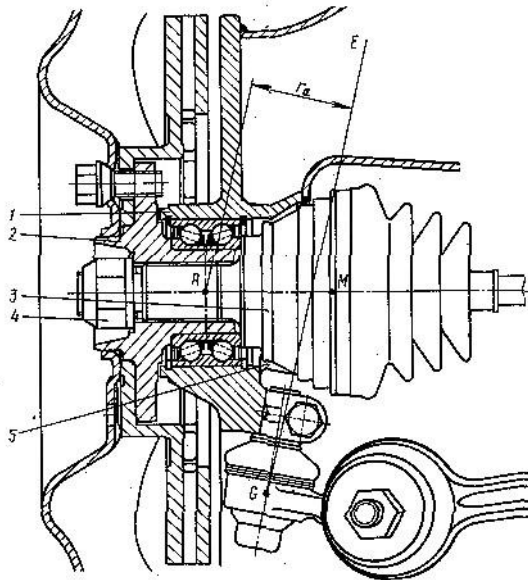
Опора переднего колеса автомобиля «Форд-Фиеста» с двумя взаимно стянутыми коническими роликовыми подшипниками; при затягивании гайки 4 устанавливается правильный зазор. Уплотнение со стороны колеса осуществляется уплотнительной манжетой 5 и шейкой 6 опоры подшипника колеса. Попадание грязи со стороны шарнира полуоси предотвращается охватывающим колпачком 2 и уплотнительной манжетой 1. Манжеты 1 и 5 имеют по две защитные кромки, работающие по периферии и по торцу
